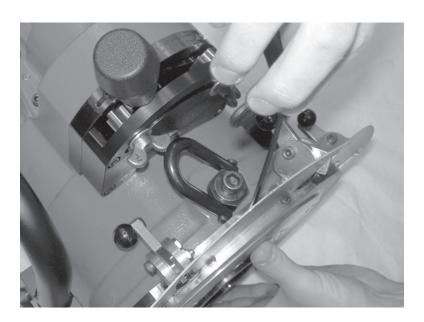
Отверните установочные винты, крепящие механизм выключателя подачи к корпусу.
